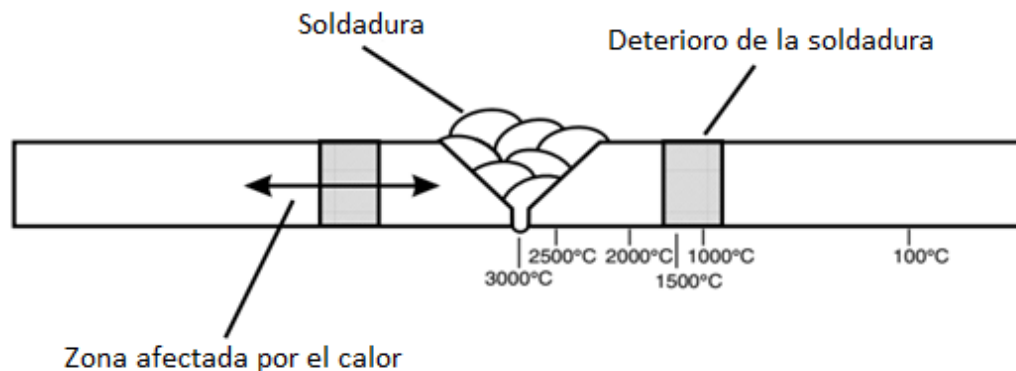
Zona de descomposición de la soldadura como una función de la temperatura de soldadura del acero (Roberge, 2007). Modificado.
